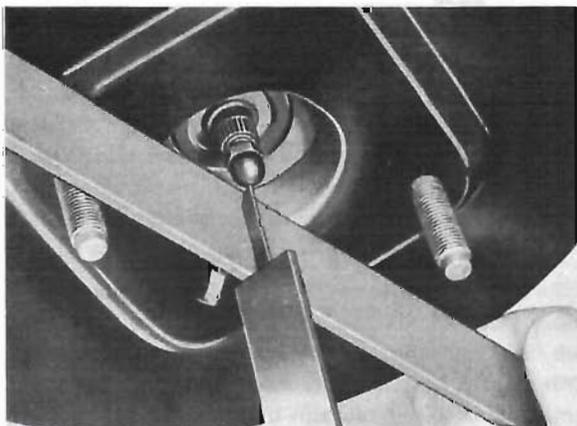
Messen der Druckstange (Höhe über Flanschebene)
